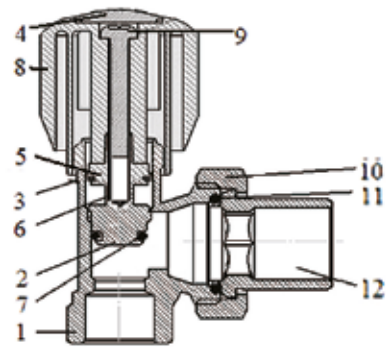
Устройство клапана ручного терморегулирующего (устройство углового и прямого клапанов идентичны)
